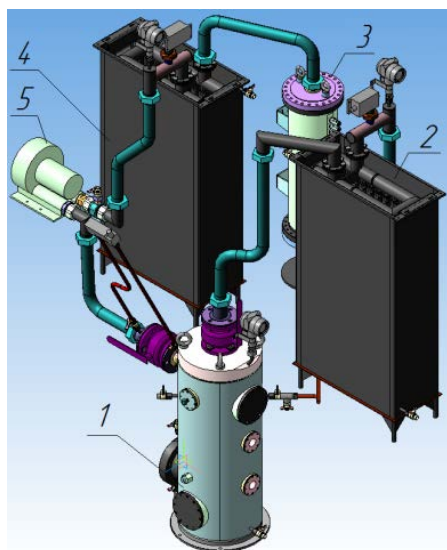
Внешний вид макета СКР: 1 – имитатор корпуса реактора; 2 – холодильник № 1, 3 – каталитический блок, 4 – холодильник № 2, 5 – воздушный компрессор
